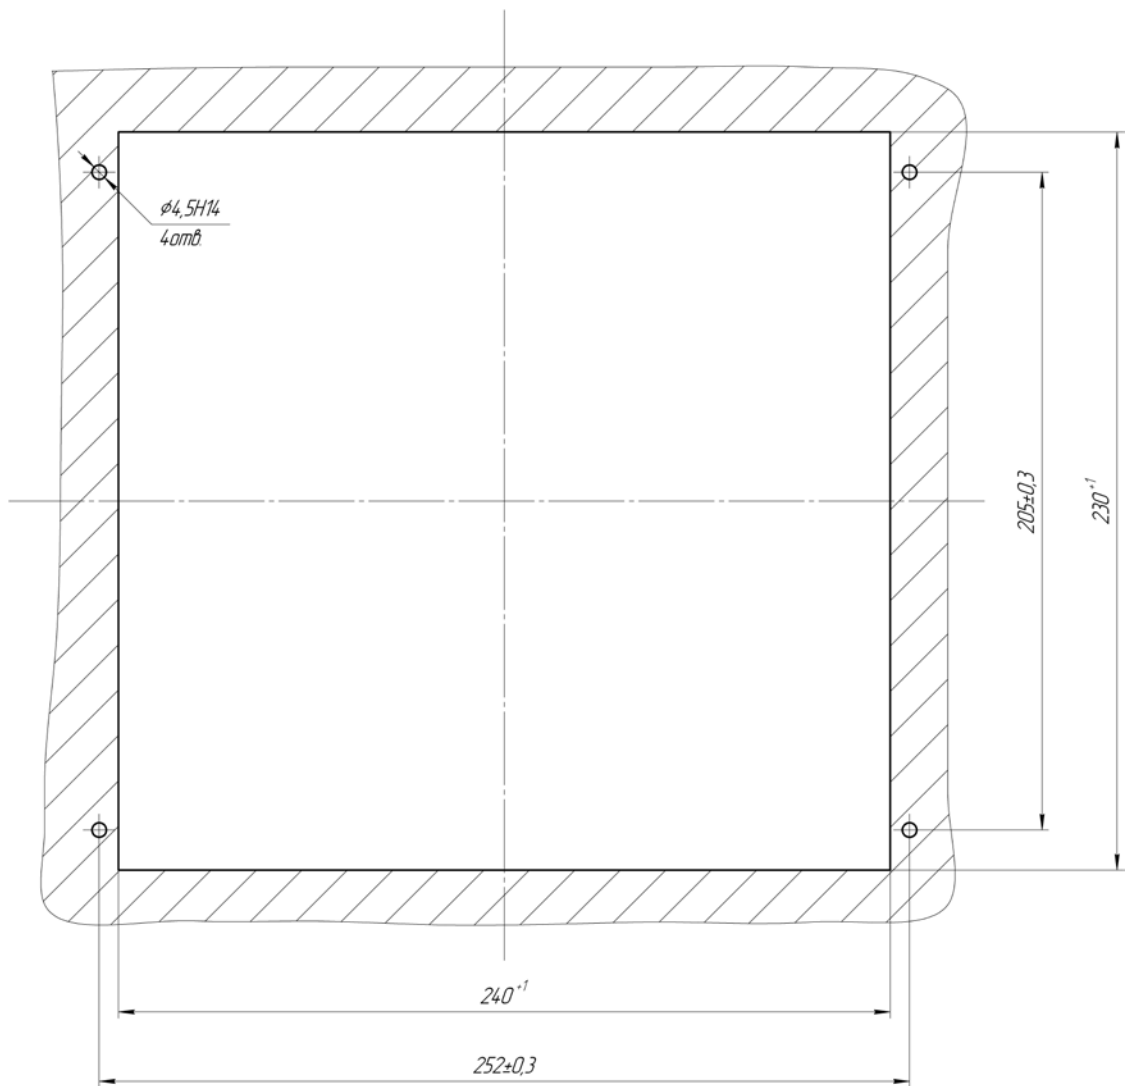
Габаритные размеры окна и крепежных отверстий для установки устройства РТН-200-05.АХ
